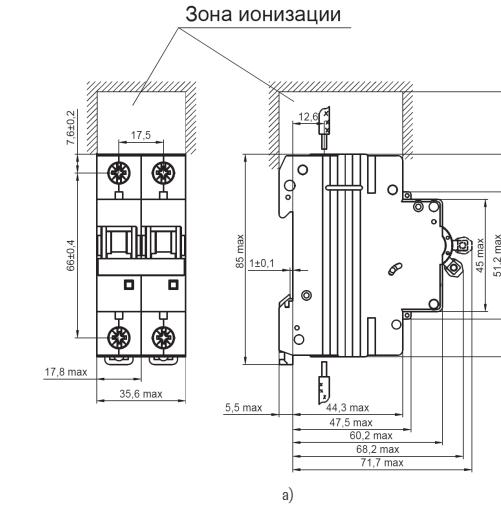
Габаритные и установочные размеры выключателей на постоянный ток
